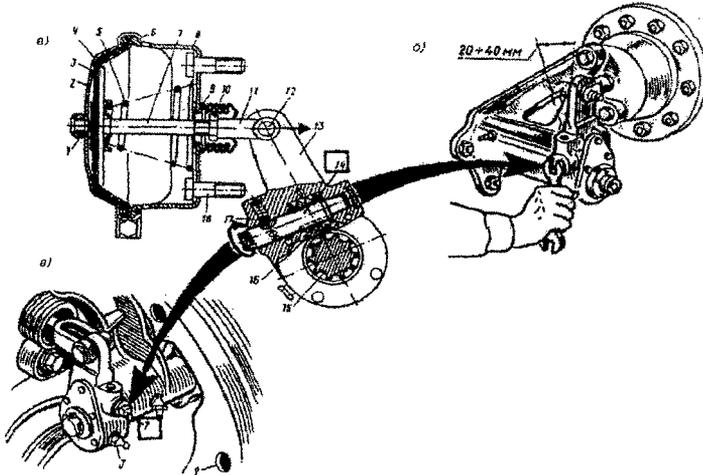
Схема частичной регулировки колесных тормозных механизмов: а – тормозная камера с регулировочным рычагом; б – регулировка колесного тормозного механизма ЗИЛ-130; в – регулировка колесного тормозного механизма КамАЗ
